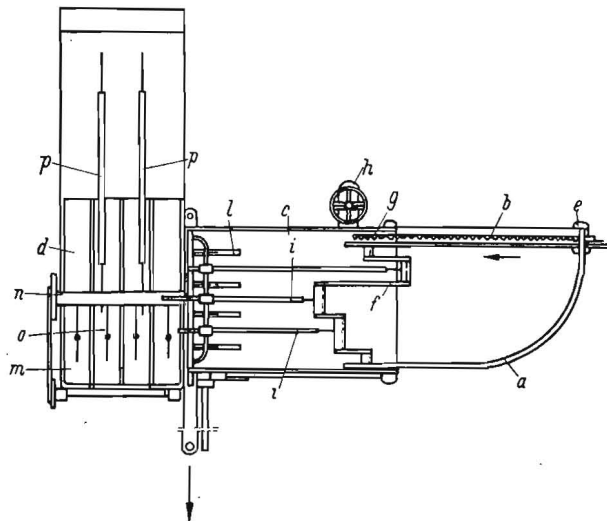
Lader für Heu, Gras und ähnliches Erntegut (Draufsicht)
